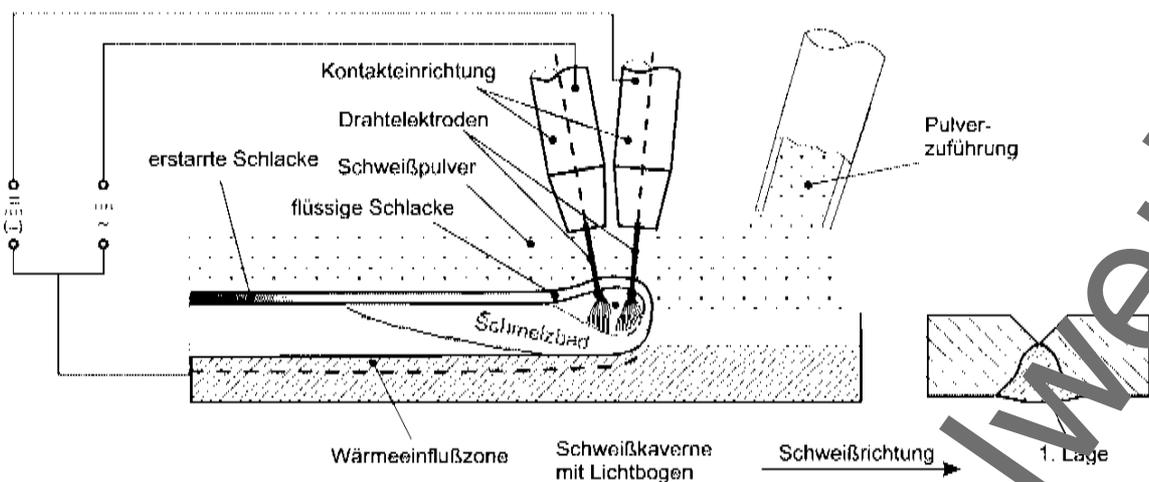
Vorgänge im Bereich der Schweißstelle beim UP-Mehrdrahtschweißen am Beispiel einer Tandemschweißanlage in Lage-/Gegenlage-Technik.
